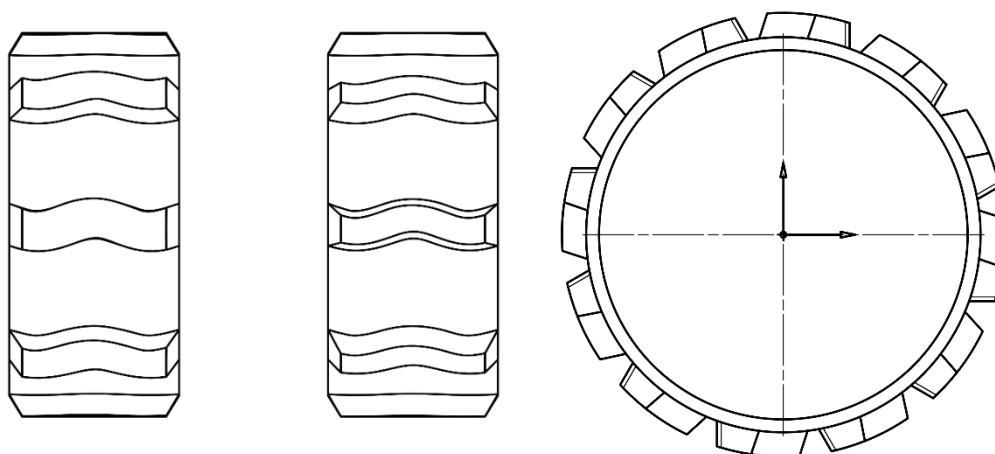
Профили лопастей колеса центратора № 3 (слева) и № 6 (центр);
